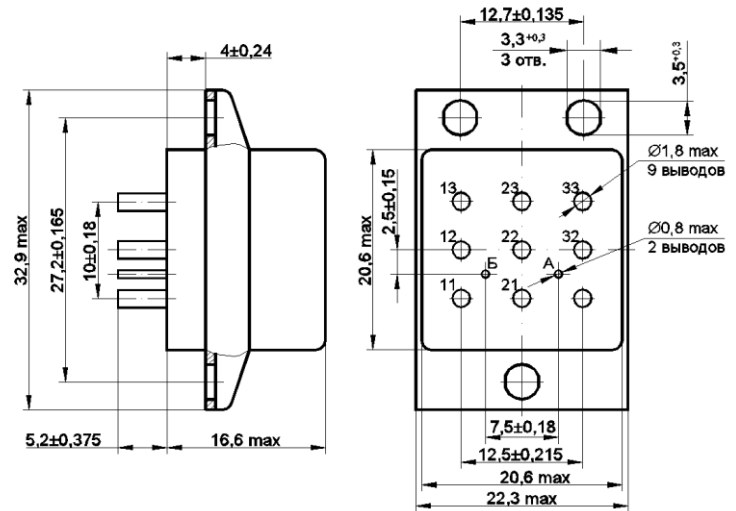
Общий вид реле исполнений РВИМ.647614.054-02, -03, -06, -07, -09, -11 с фланцем с габаритными, установочными и присоединительными размерами
